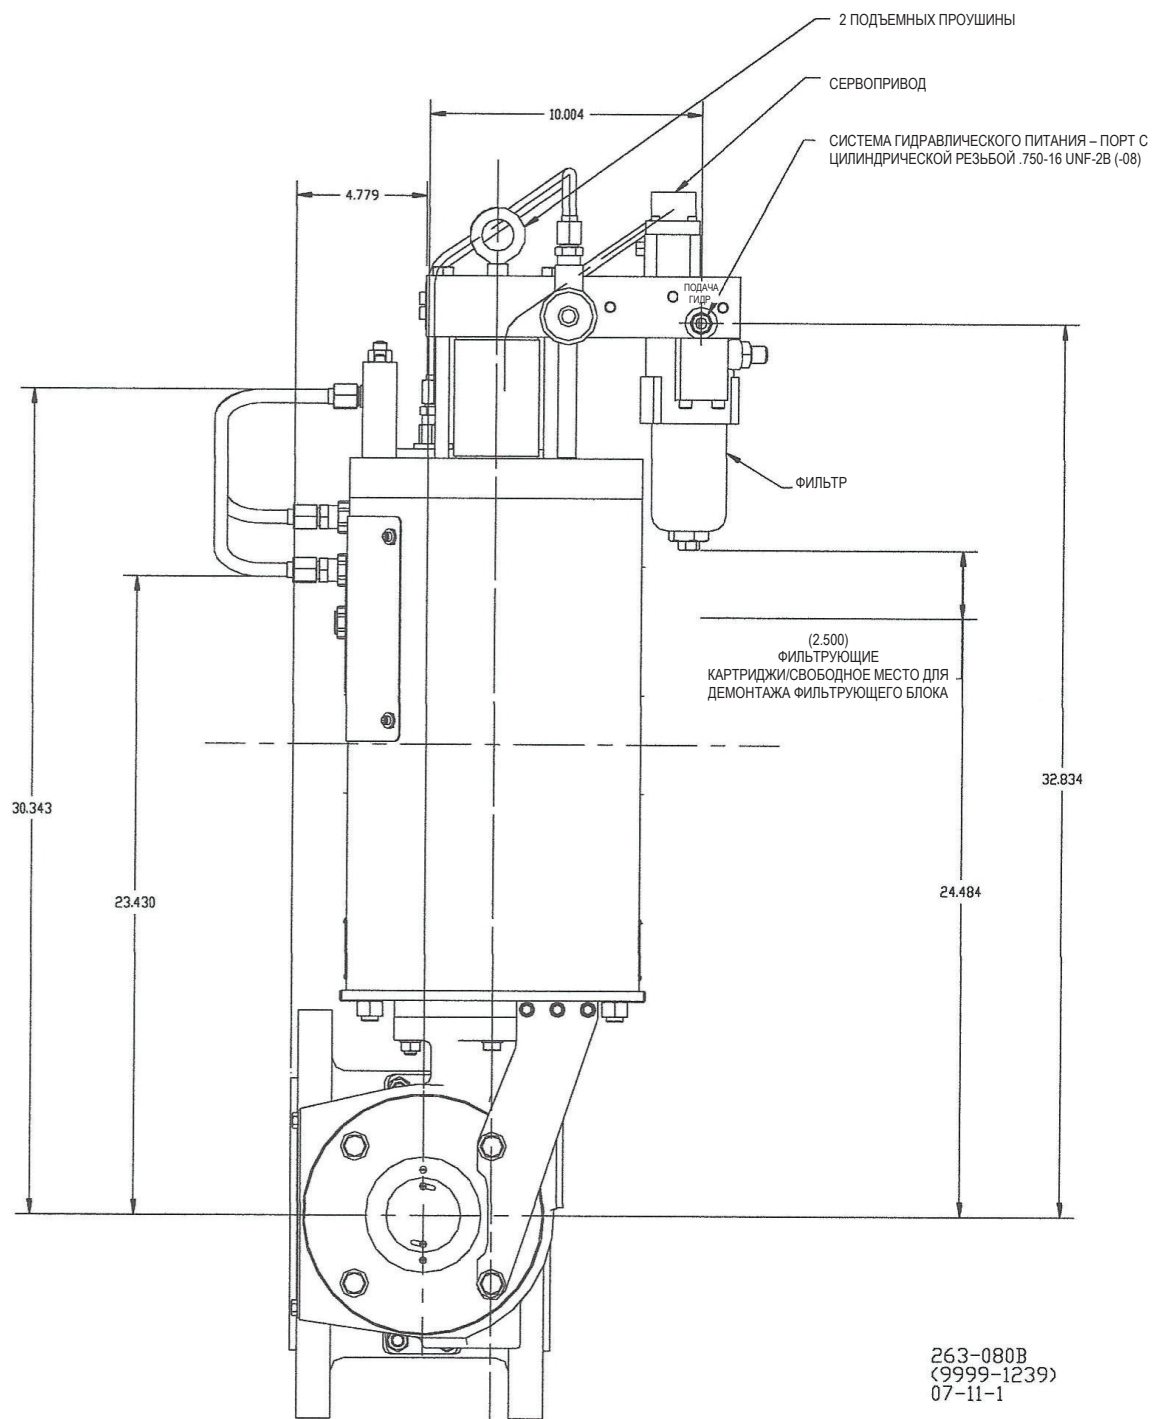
Габаритный чертеж 8" запорно-регулирующего газового клапана
